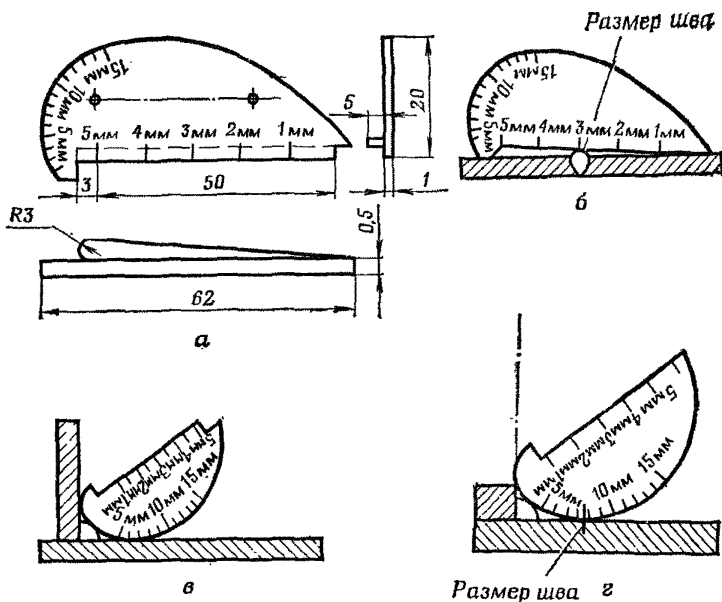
Универсальный шаблон Красовского для проверки формы и размеров сварных швов:
